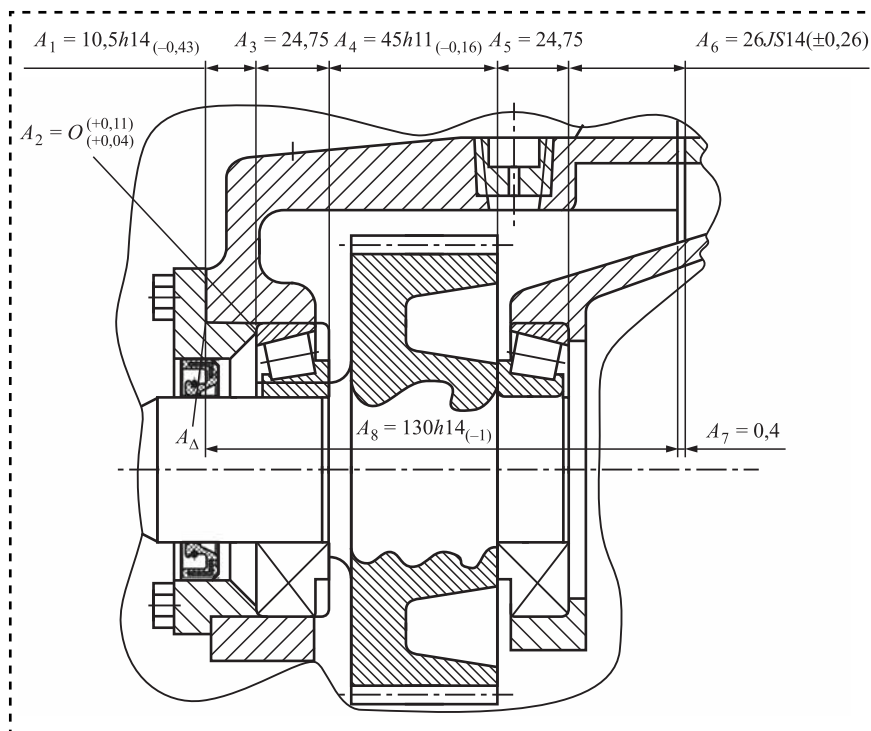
Выходной вал редуктора 4МЦ2С-80
